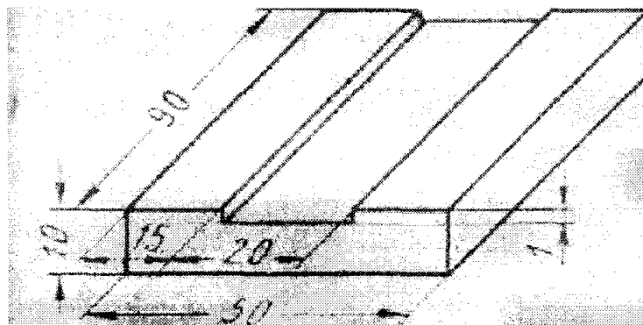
Подготовка канавки на поверхности стальной пластины, наплавляемой сормайт
